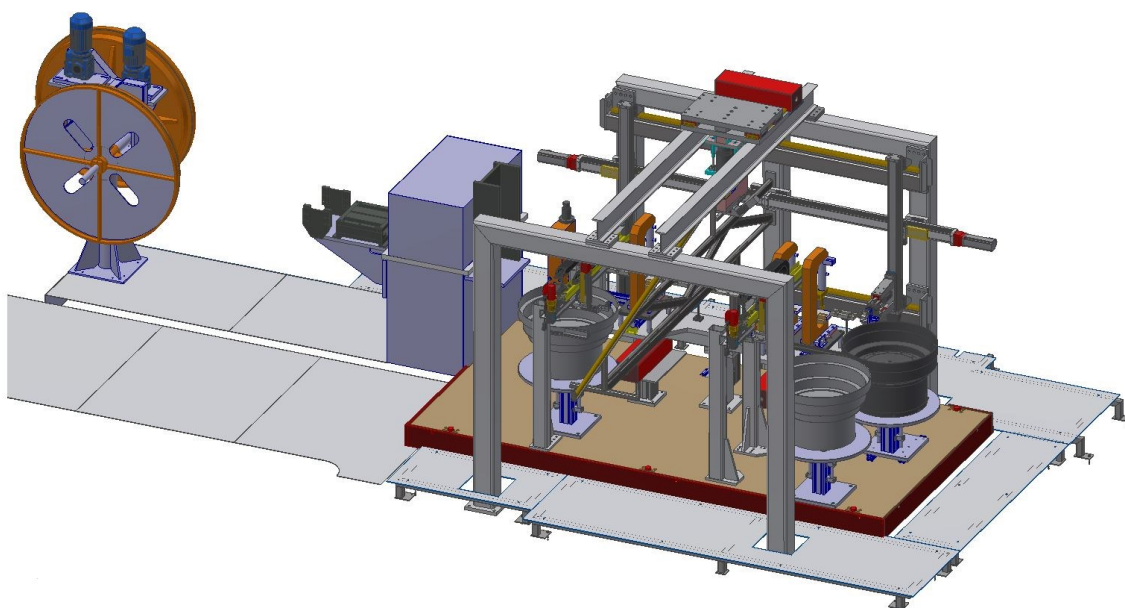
Stáčecí mechanismus s obrácenou svařovací pozicí
